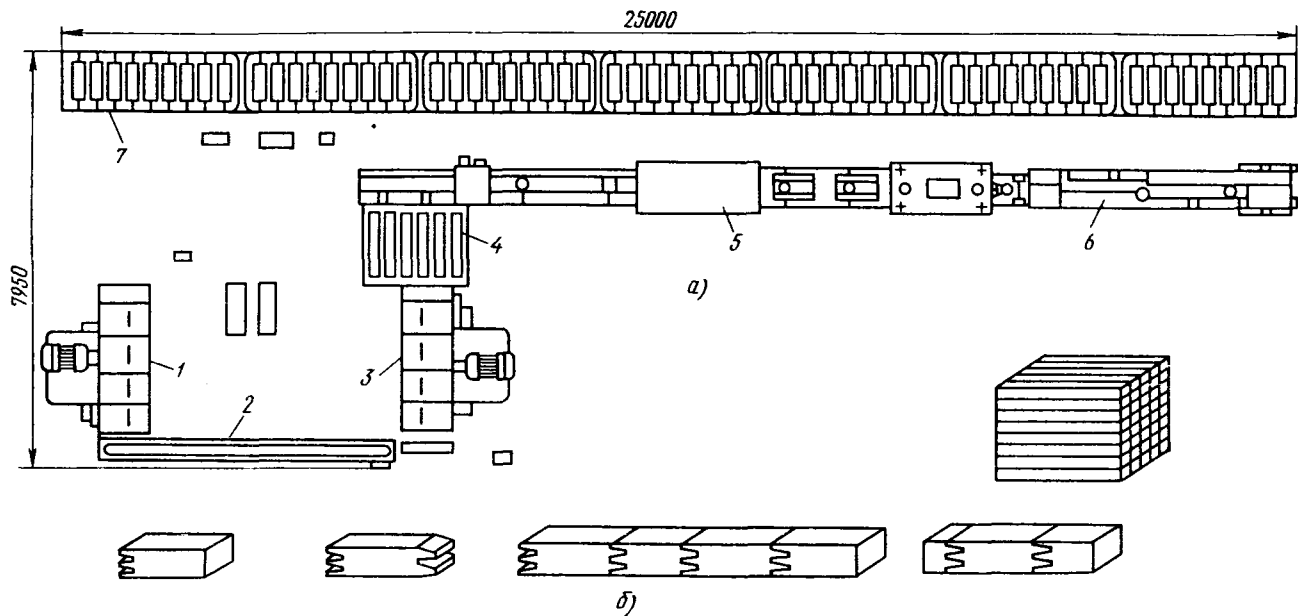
Схема полуавтоматической линии ДВ202 склеивания брусковых деталей по длине на зубчатый шип:
